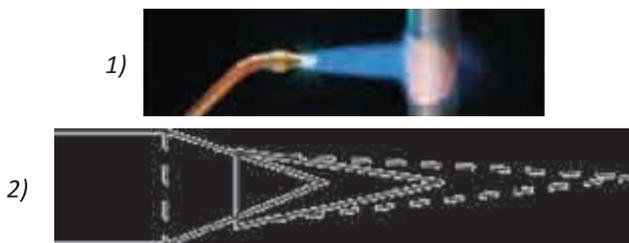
Оптимальный вид пламени горелки для пайки твердым припоем:
